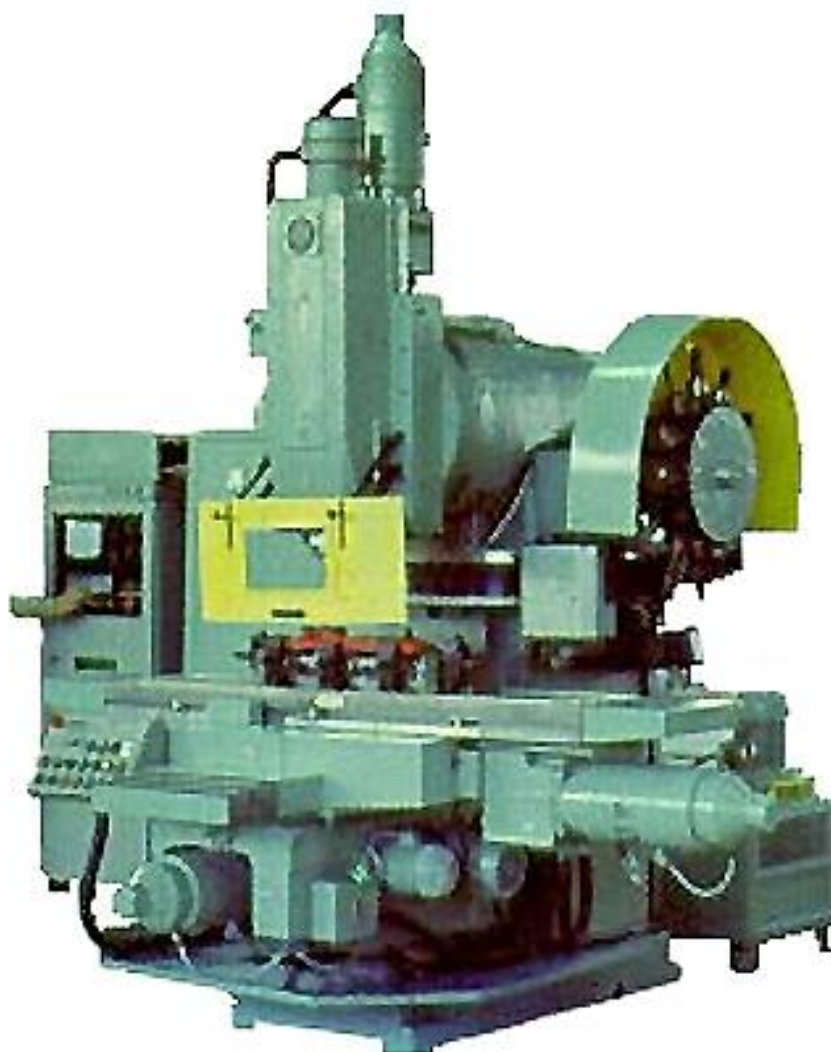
Вертикальный станок с магазином типа «РУКА» и диском с инструментами
